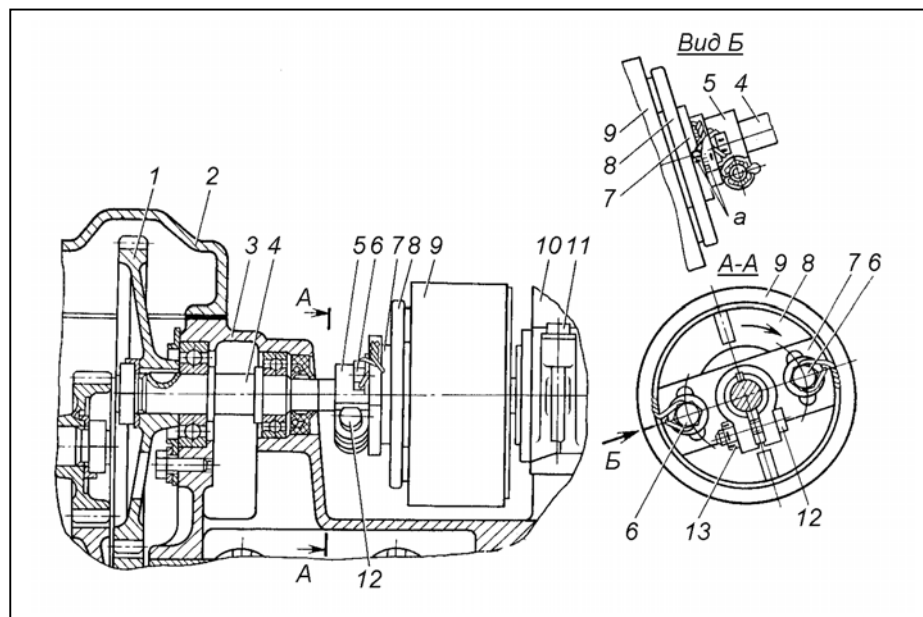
Соединение муфты привода ТНВД двигателей ЯМЗ-236,-238 (для модиф., снятых с производства): 1 – ведомая шестерня привода ТНВД; 2) – верхняя крышка блока; 3 – блок цилиндров; 4 – вал; 5 – фланец полумуфты; 6, 11 – болты; 7 – полумуфта; 8 – шайба полумуфты; 9 – АМОВ; 10 – ТНВД; 12 – стяжной болт фланца полумуфты; 13 – гайка; а – риски на фланце и метка на полумуфте.
